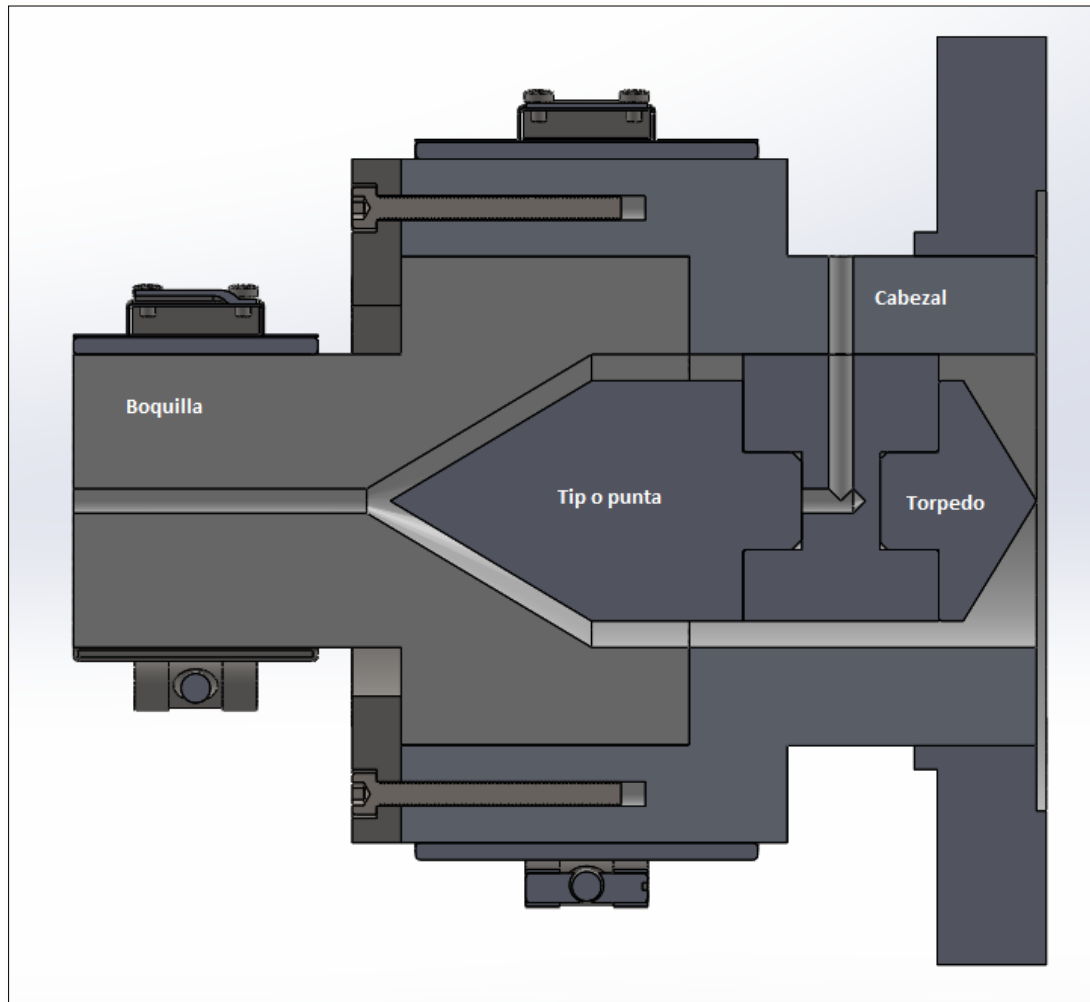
Vista en corte de cabezal para extrusión de filamentos.
